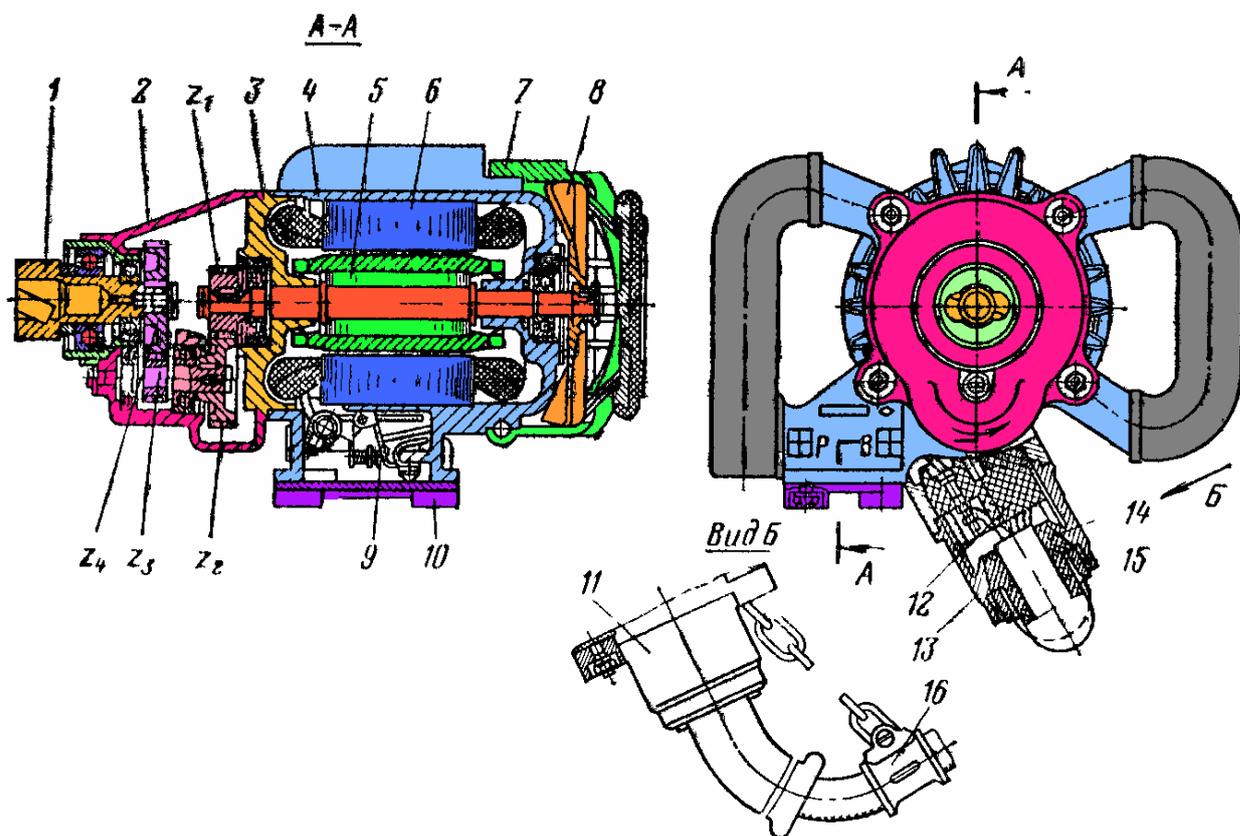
Конструкция ручного сверла СЭР-19М
